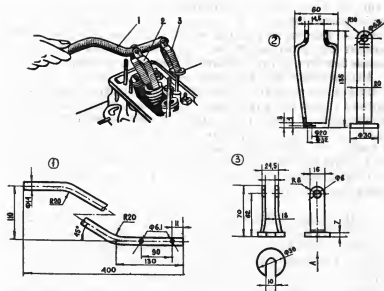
Приспособление для сжатия пружин клапанов: 1 — рычаг; 2 — упор, сжимающий пружины клапана; 3 — упор, фиксируемый на шпильке гайкой, крепящей корпус распределительного вала.
